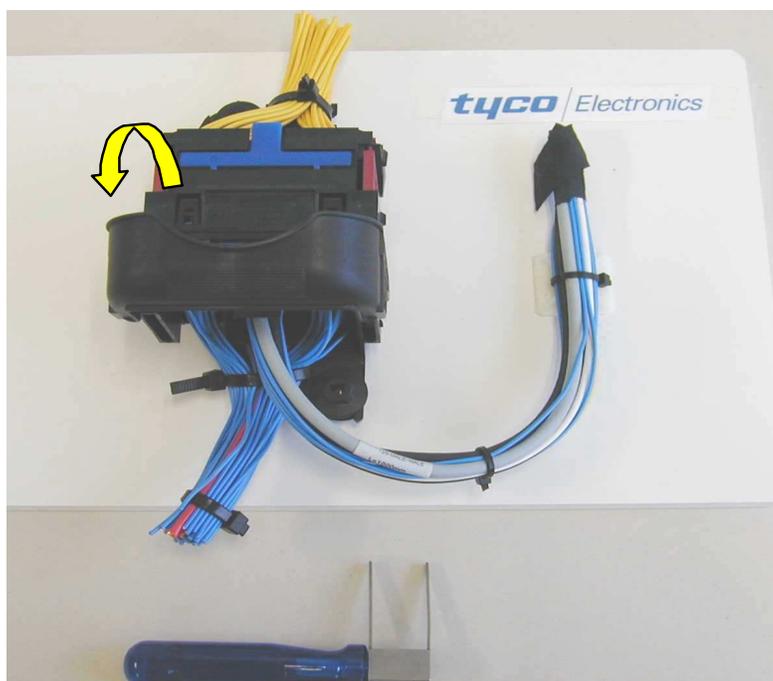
Hebel aus Endposition lösen und bis zum Anschlag (90°) aufschwenken.
